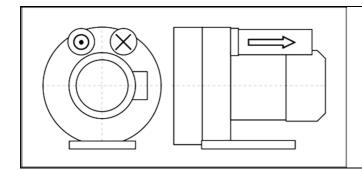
Двухпоточнаяконструкция вакуумного насоса/компрессорас двумя рабочими колесами.
